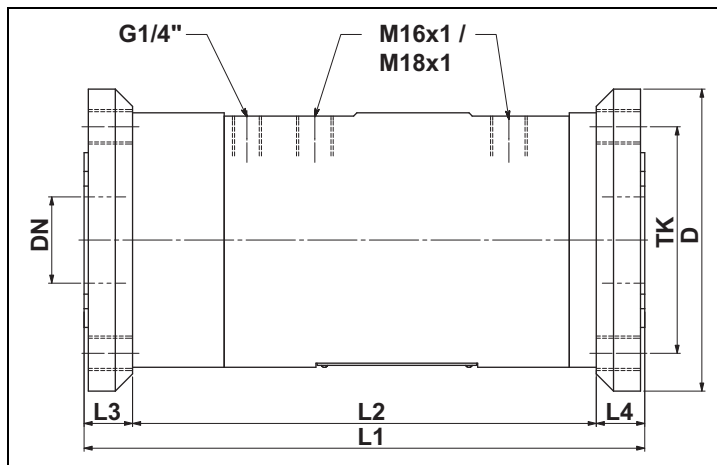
Maßzeichnung OMP mit ANSI-Flansch
